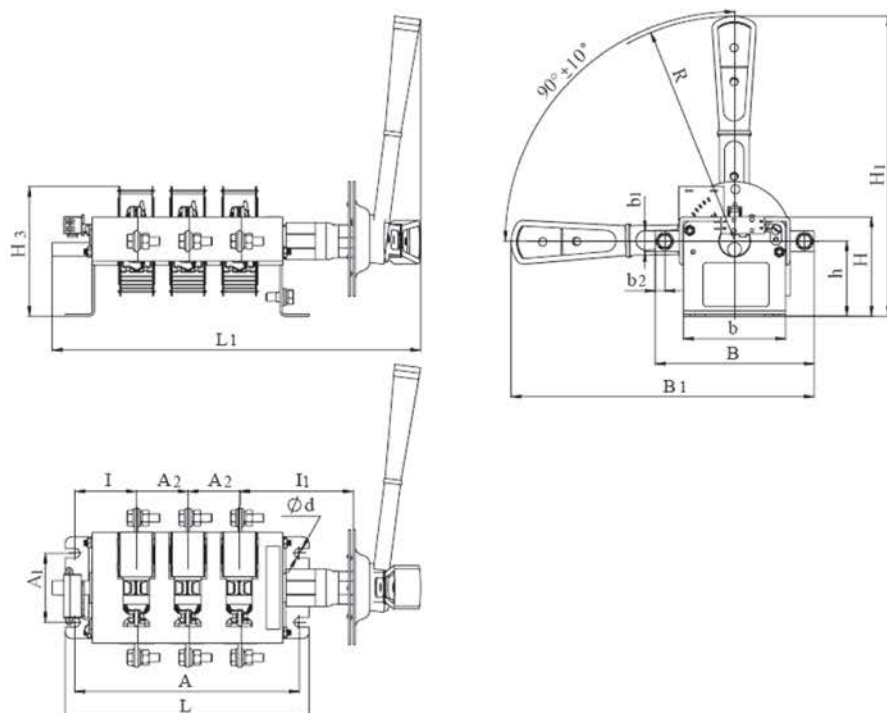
Выключатель-разъединитель трехполюсный на одно направление с боковой несъемной рукояткой.
